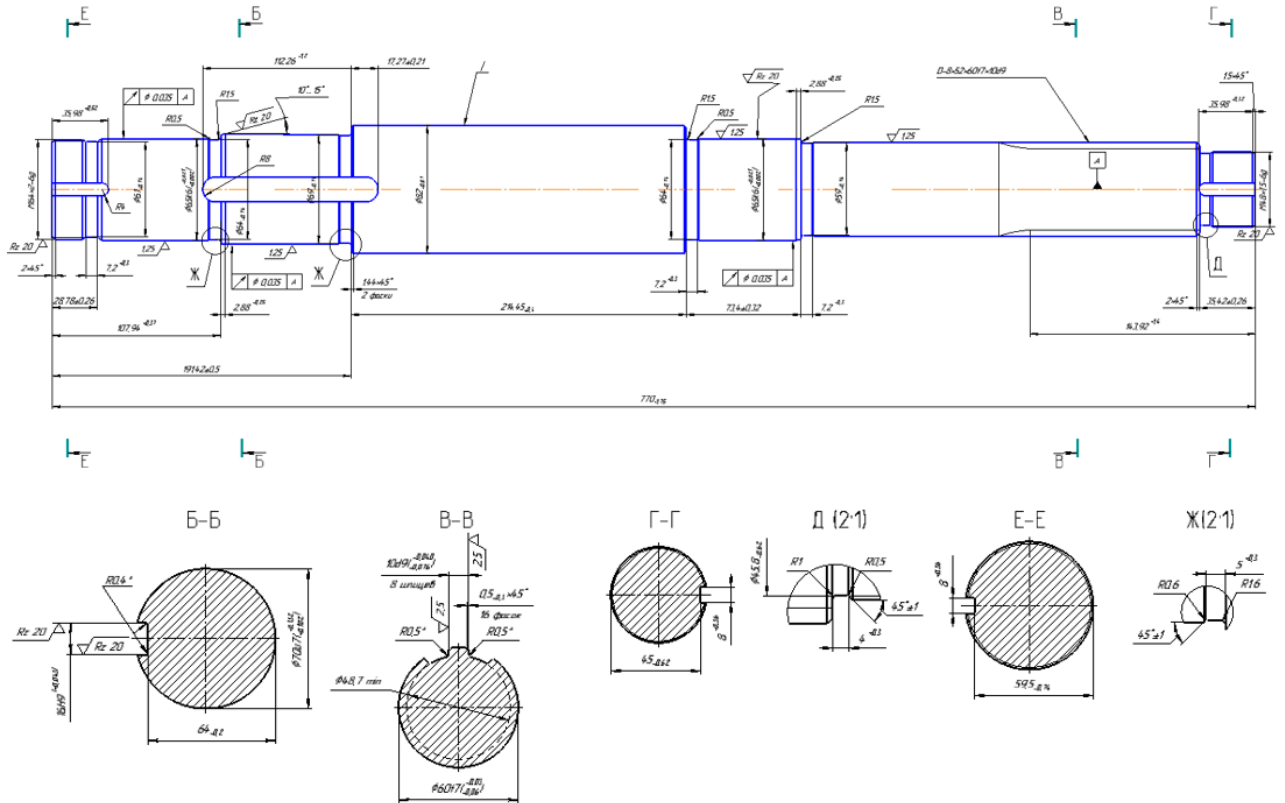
Загальний вигляд деталі «Великогабаритний вал Ø82 × 770 мм»
